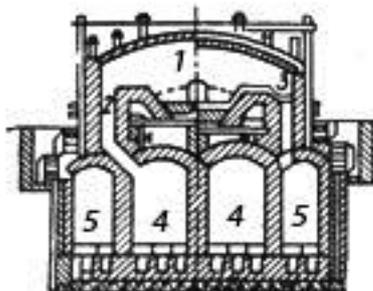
Регенеративна зварювальна піч для стикової зварки труб
